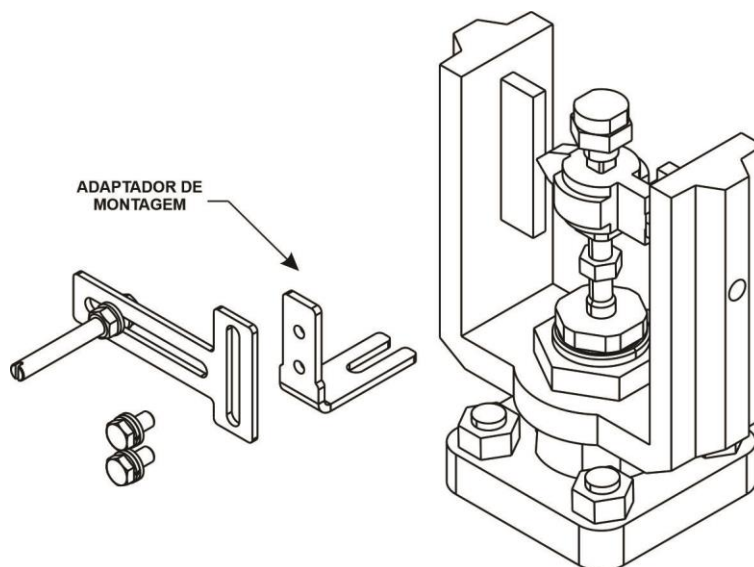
Conjunto de realimentação montado com adaptador de montagem
